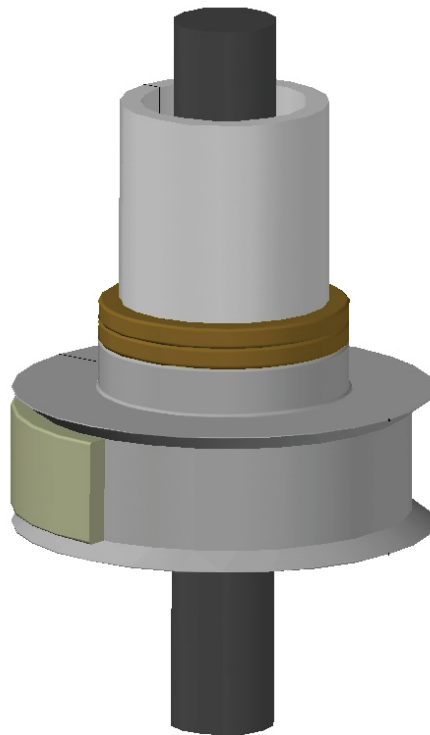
Imagem 3D do conjunto montado no fuso (Fonte: Próprio autor)
